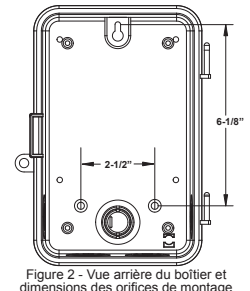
Vue arrière du boîtier et dimensions des orifices de montage
